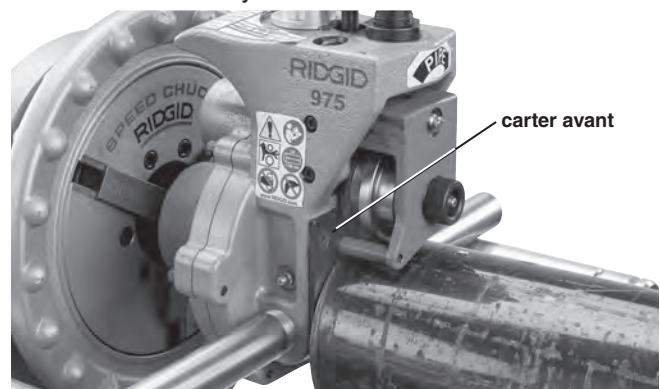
Engagement du tuyau sur l'arbre de transmission jusqu'à fleur du carter avant
